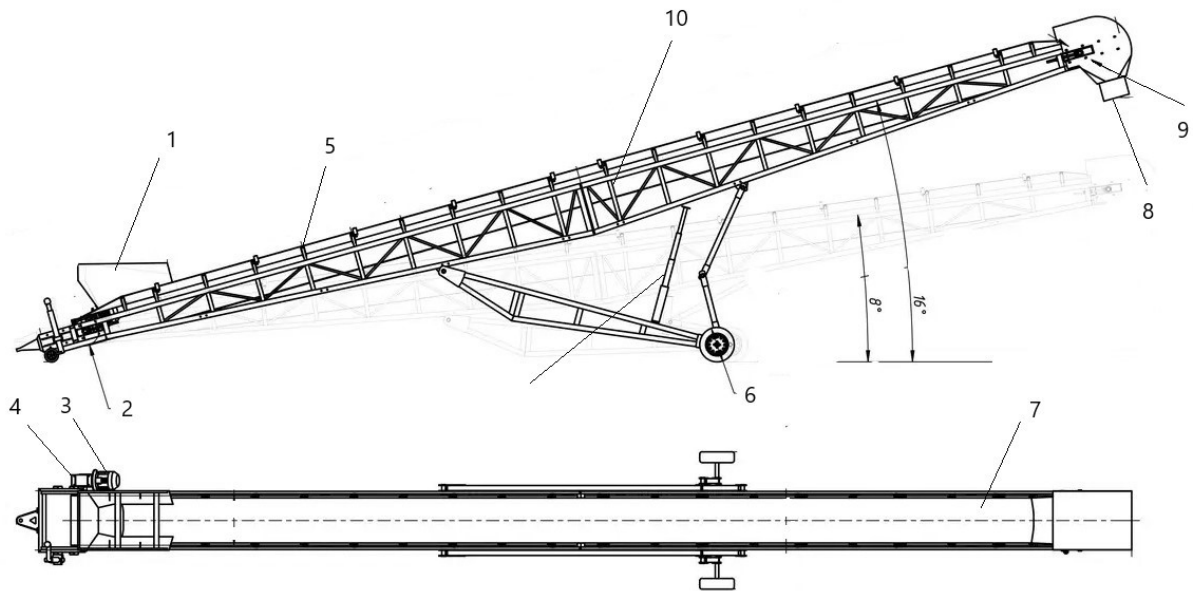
Конструкція стрічкового транспортеру СТМН-18-100.
